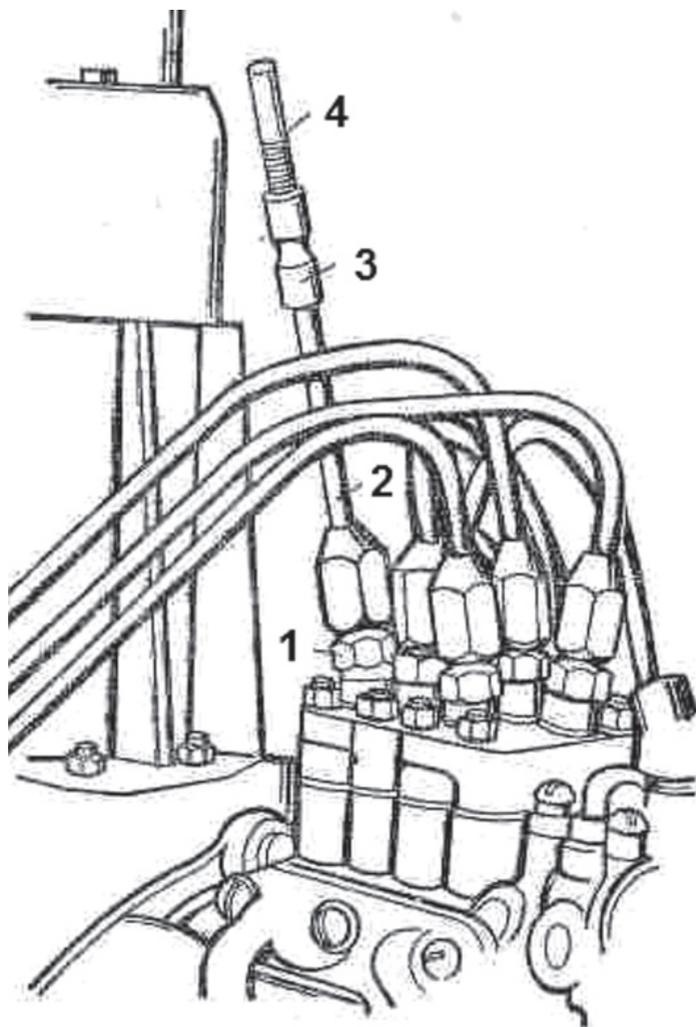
Проверка установочного угла опережения подачи топлива:
